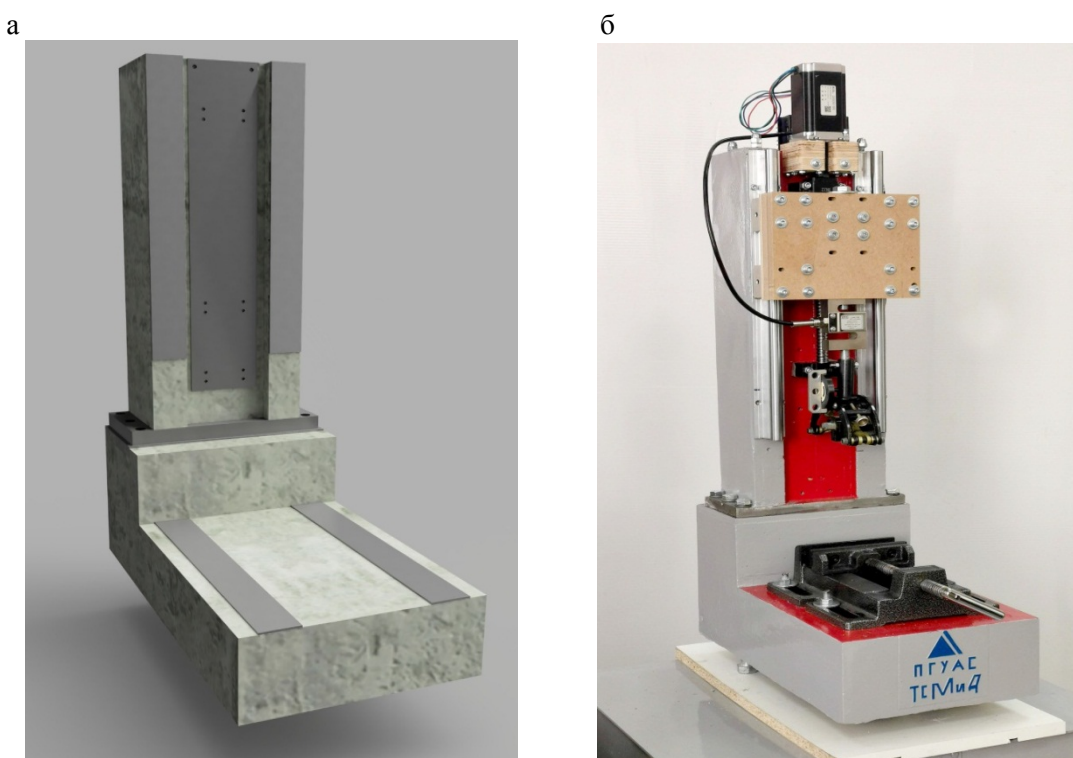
Общий вид цифровой трехмерной модели станины и изготовленной установки:
